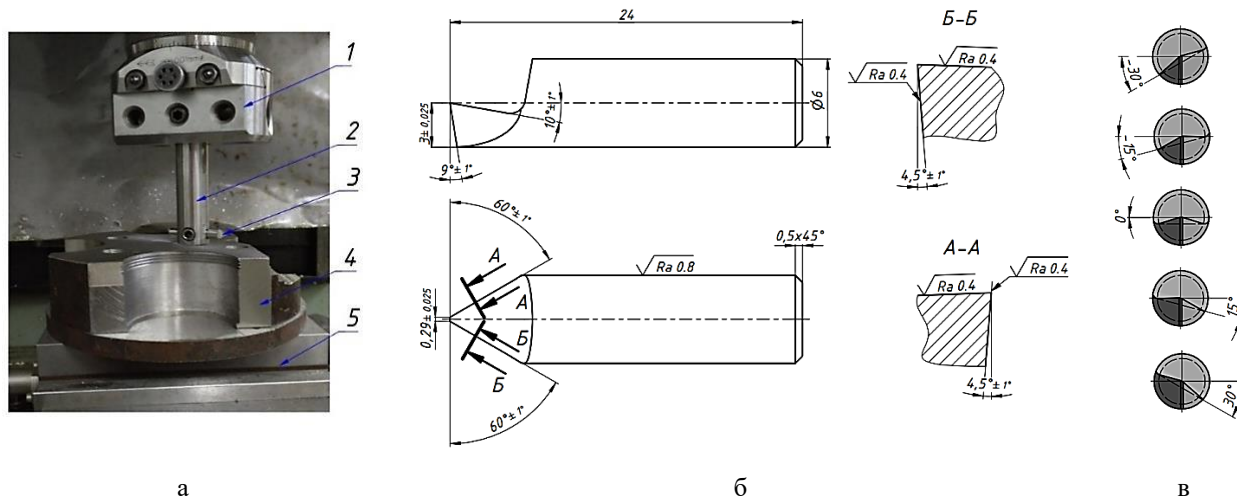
Инструментальная система для измерения составляющих силы резания: а – общий вид: 1 – расточная головка; 2 – державка; 3 – резьбовой резец; 4 – заготовка; 5 – динамометрическая система; б – параметры резьбового резца; в – вид резца при разных углах наклона режущей кромки на фасочной части ω
